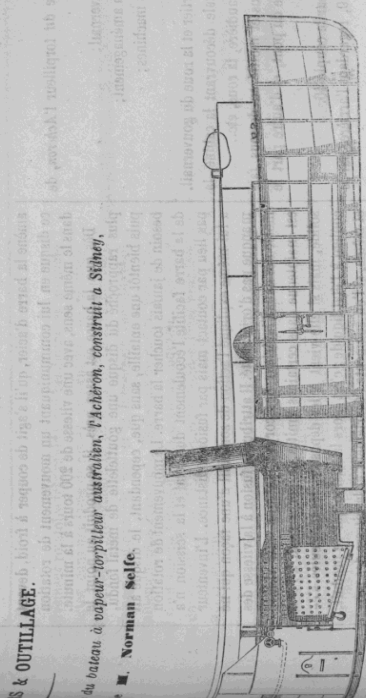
Coupe longitudinale du torpilleur l'Achéron.
